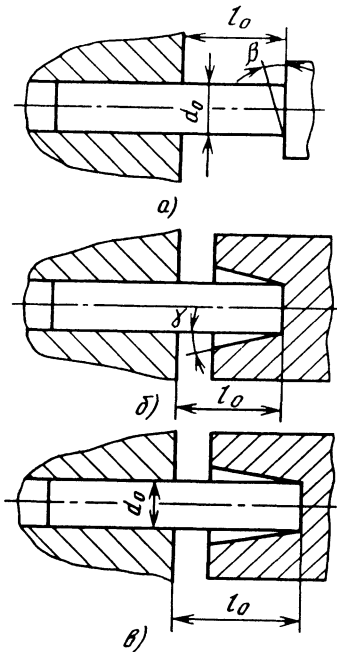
Положения заготовительных пуансонов с различной формой рабочего ручья в начале первого перехода высадки
